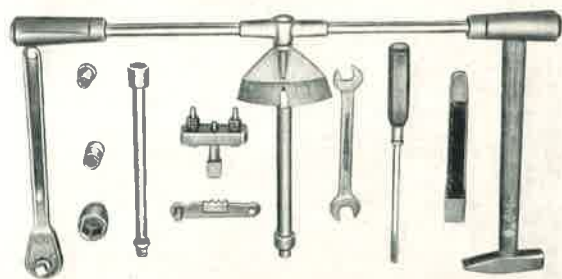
Zusammenstellung der Werkzeuge, wie sie für die Arbeit Gruppe M Motor M 23 gebraucht werden.
